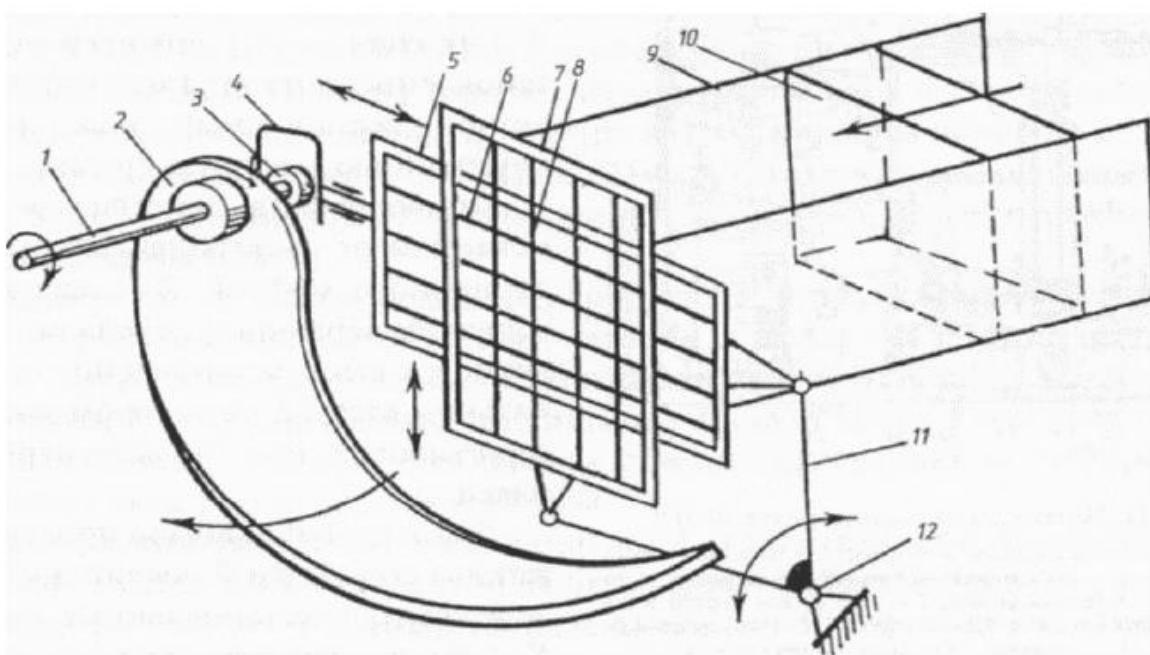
Схема режущего и подающего механизмов шпигорезки:
